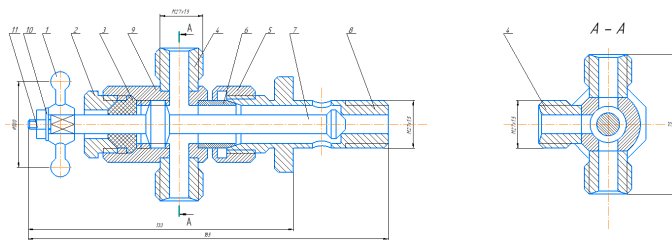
Приспособление для включения агрегатов гидросистемы
